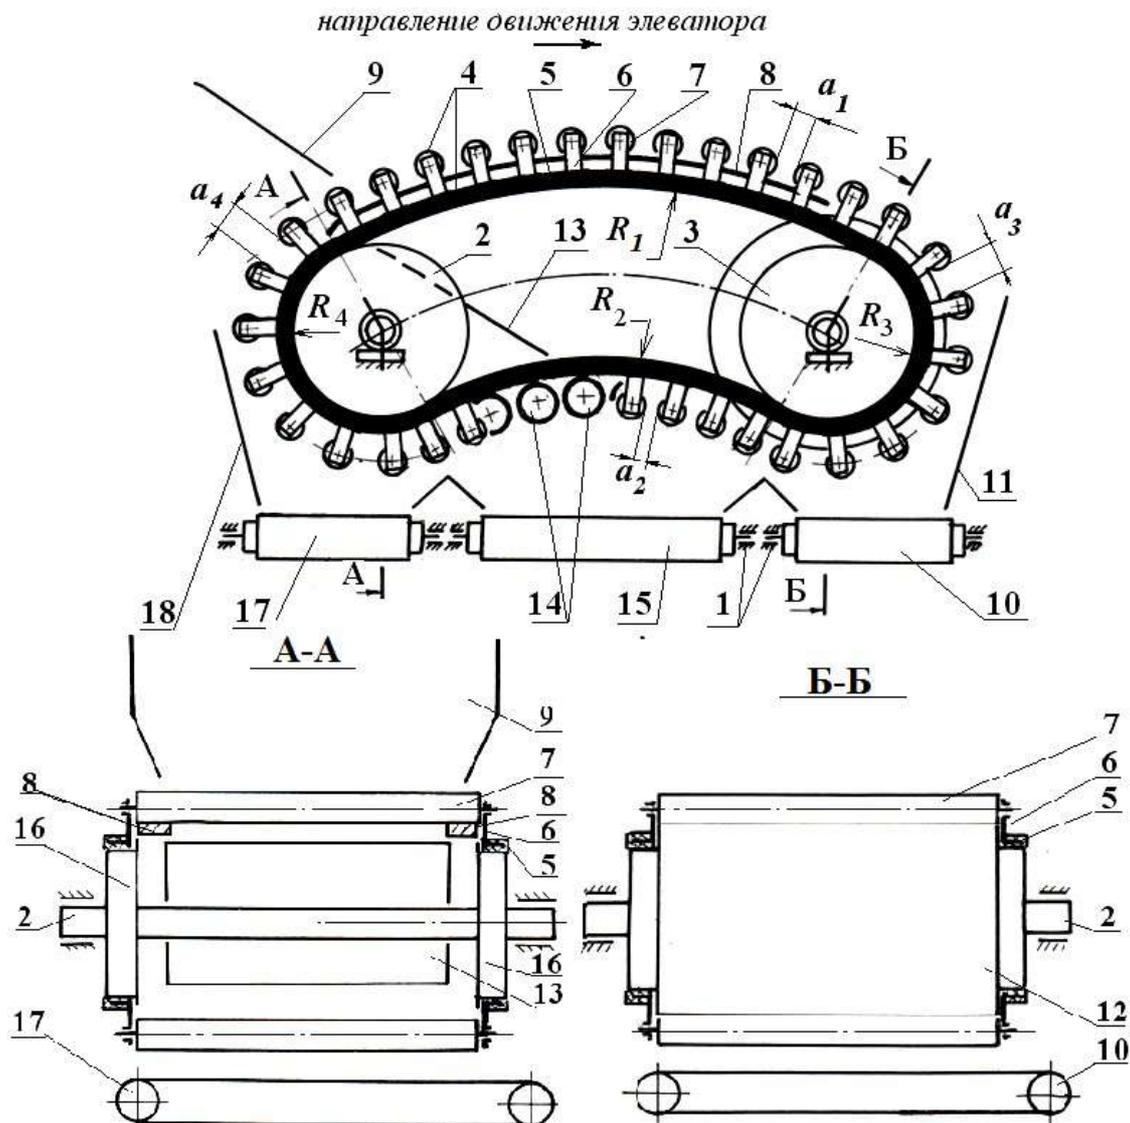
Схема РСМ: 1- рама; 2 и 3- барабаны; 4- элеватор; 5- замкнутая лента (цепь); 6- кронштейны консоли; 7- ролики; 8- выпуклая поверхность (дорожка для привода роликов) верхней ветви замкнутой ленты; 9- приемная скатная доска; 10, 15 и 17- транспортеры для крупной, мелкой и средней фракций; 11 и 18 - ограждения крупной и средней фракций; 12 и 13 – сплошной и полый барабаны; 14- роликовая вогнутая поверхность для нижней ветви; 16- шкив
